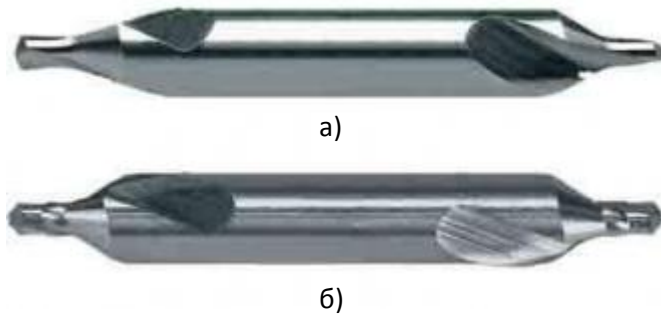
Центрувальні свердла: а - звичайне; б - із запобіжним конусом
